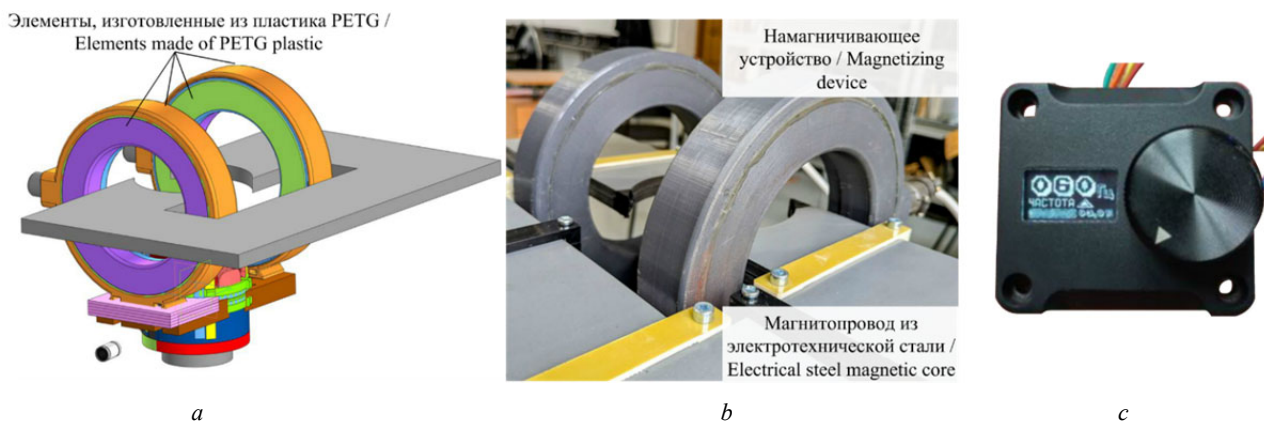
Намагничивающее устройство для контроля серийных деталей:
